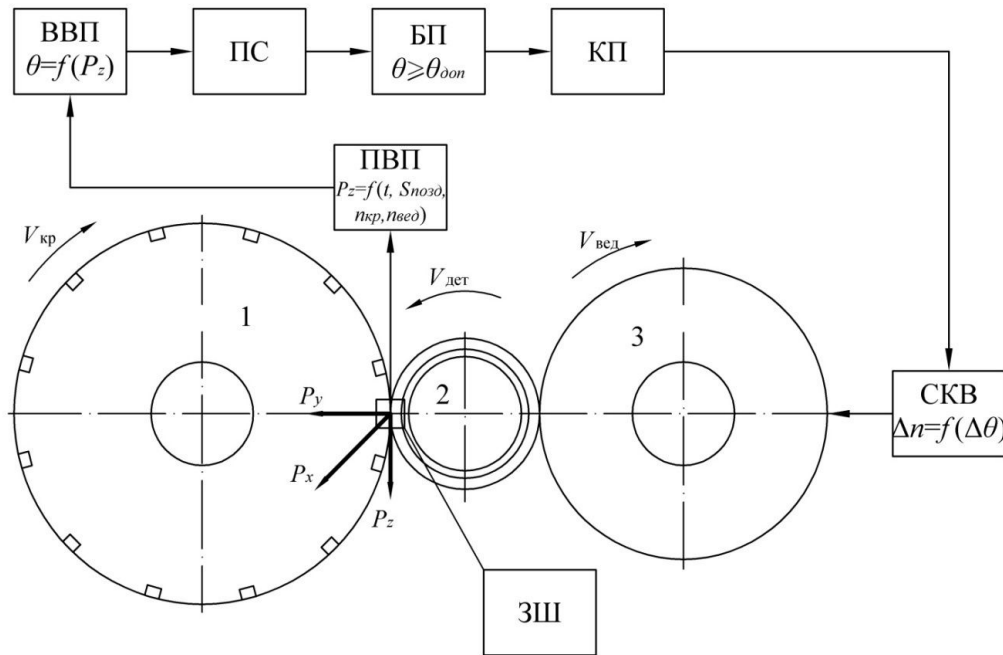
Система адаптивного керування температурою шліфування на базі безцентрово-шліфувального верстату SASL5AD: 1 – шліфувальний круг; 2 – заготовка; 3 – ведучий круг; ЗШ – зона шліфування; ПВП – первинний вимірювальний перетворювач; ВВП – вторинний вимірювальний перетворювач; ПС – підсилювач сигналу; БП – блок порівняння; КП – керуючий прилад; СКВ – система керування верстату;  $\Delta n$  – зміна частоти обертання ведучого круга, яка необхідна для забезпечення необхідного значення тангенціальної сили  $\Delta P_z$ ;  $\Delta \theta$  – регульована температура
